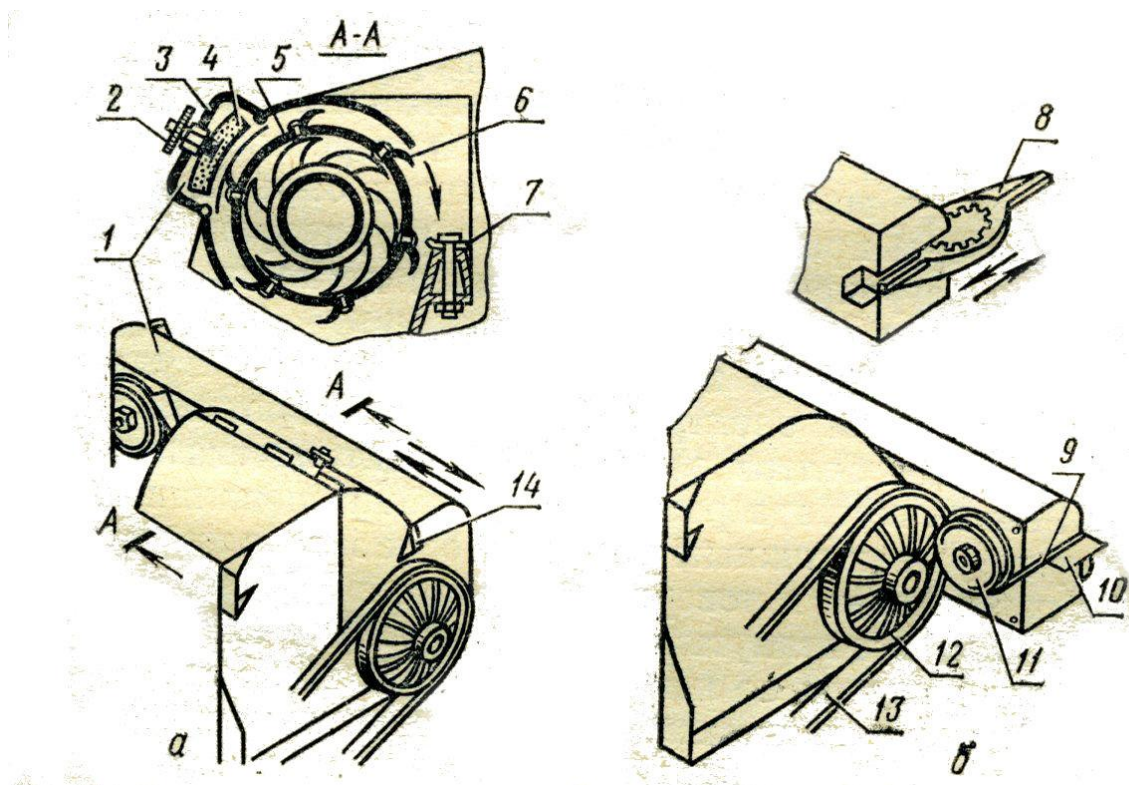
Схема заточки ножей: режущего барабана (а) и аппарат вторичного резания (б): 1-корпус; 2-штурвал; 3-обойма; 4-камень; 5-режущий барабан; 6 и 7-нож и противорежущая пластина; 8-подвижный нож аппарата вторичного резания; 9-наждачный камень; 10-подручник; 11-фрикционное кольцо; 12-шкив привода режущего барабана; 13-ремень; 14-запорная заслонка.
